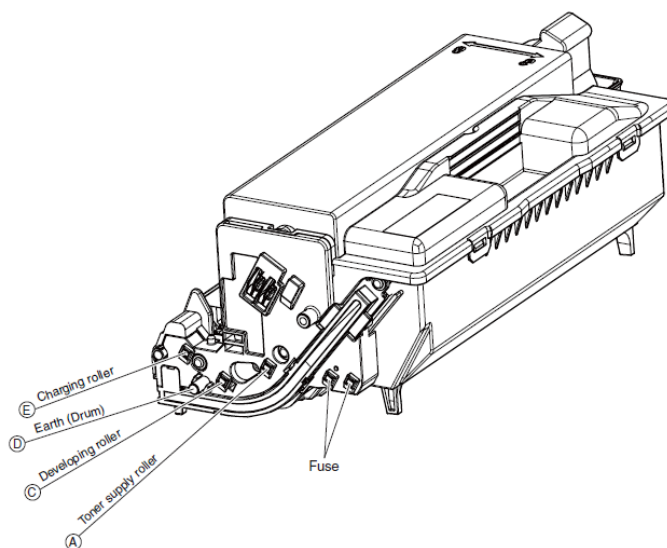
Розташування контактів вала проявлення (Developing roller)
